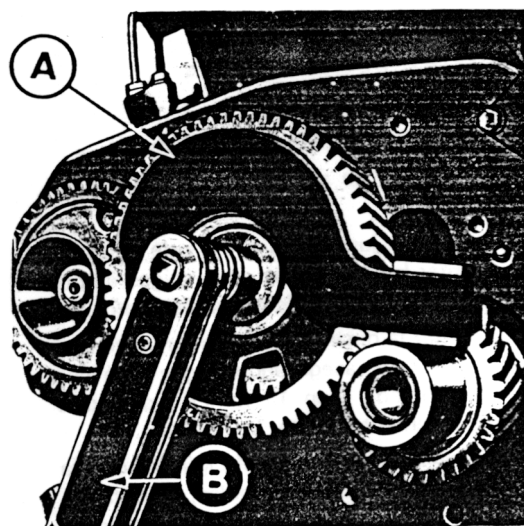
A-14E-01 fijación de los engranajes del árbol de levas
